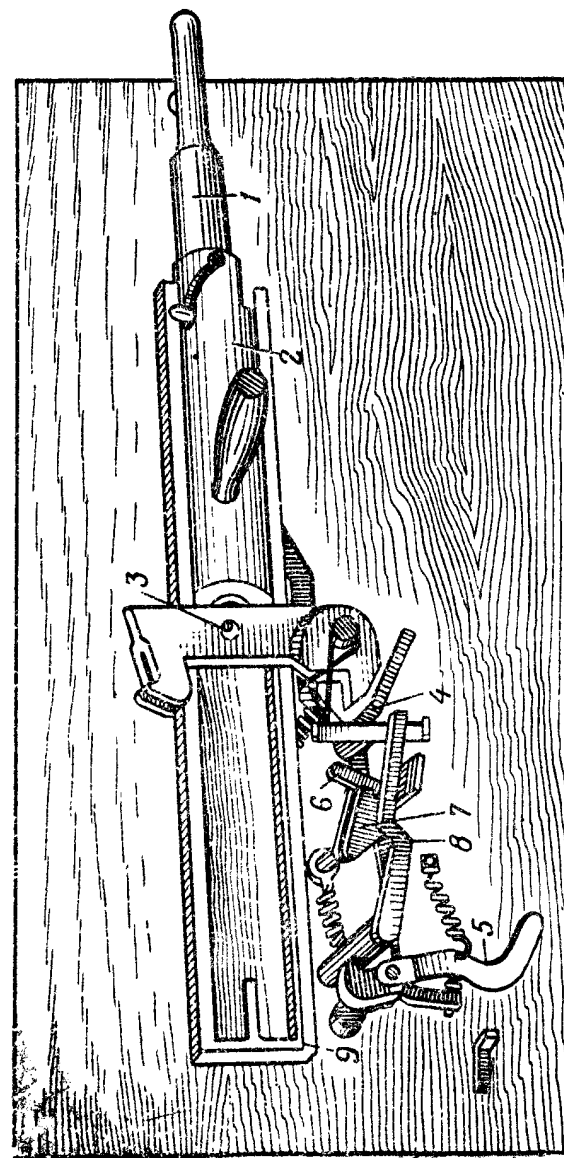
Макет ударно-спускового механизма снайперской винтовки Драгунова (СВД):
